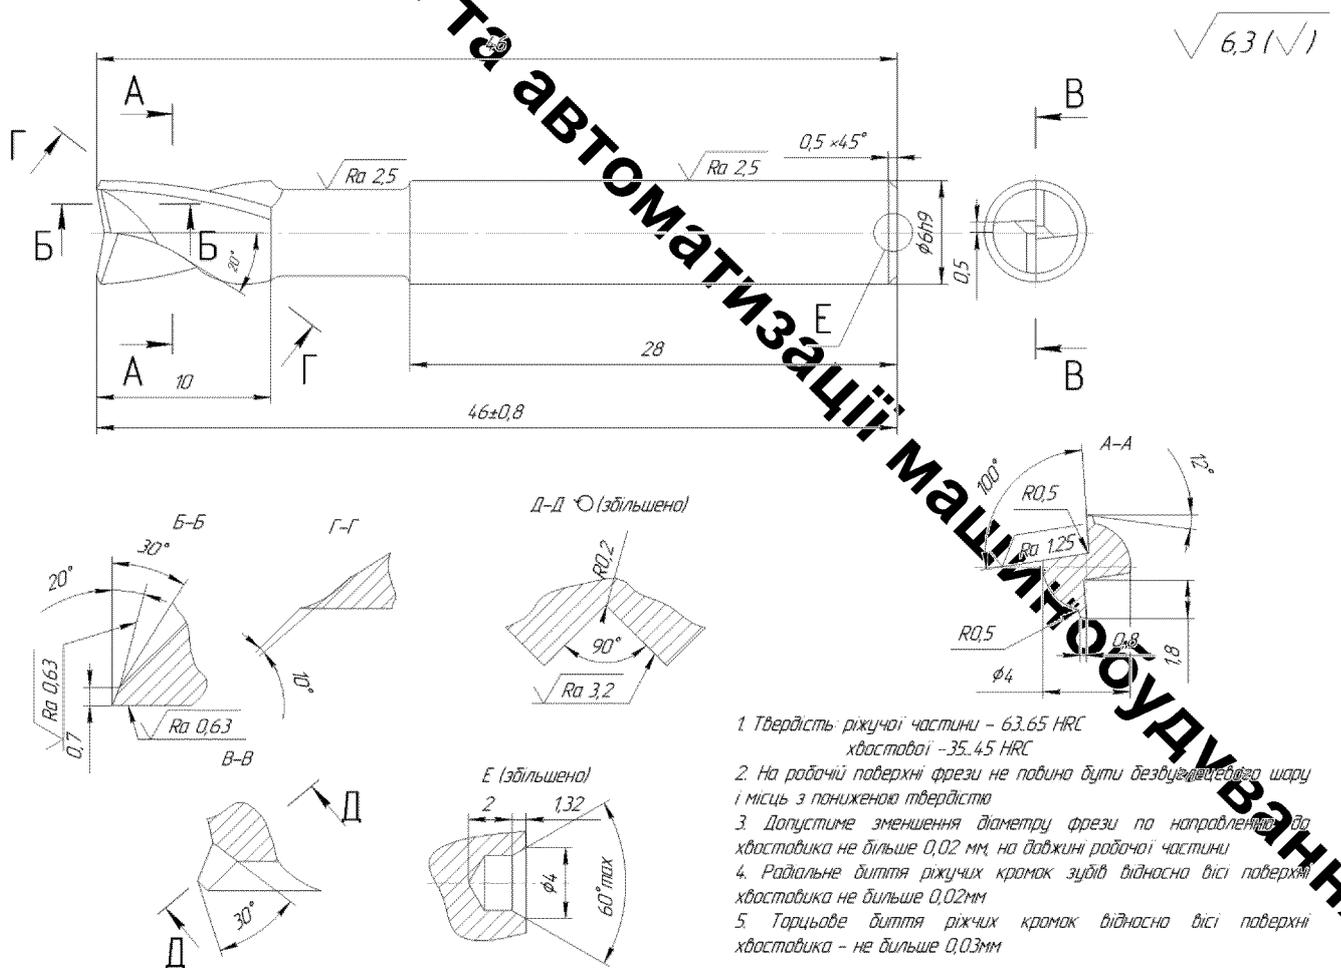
Конструкція спроектованої шпонкової фрези для обробки шпонкового пазу В=6Р9
